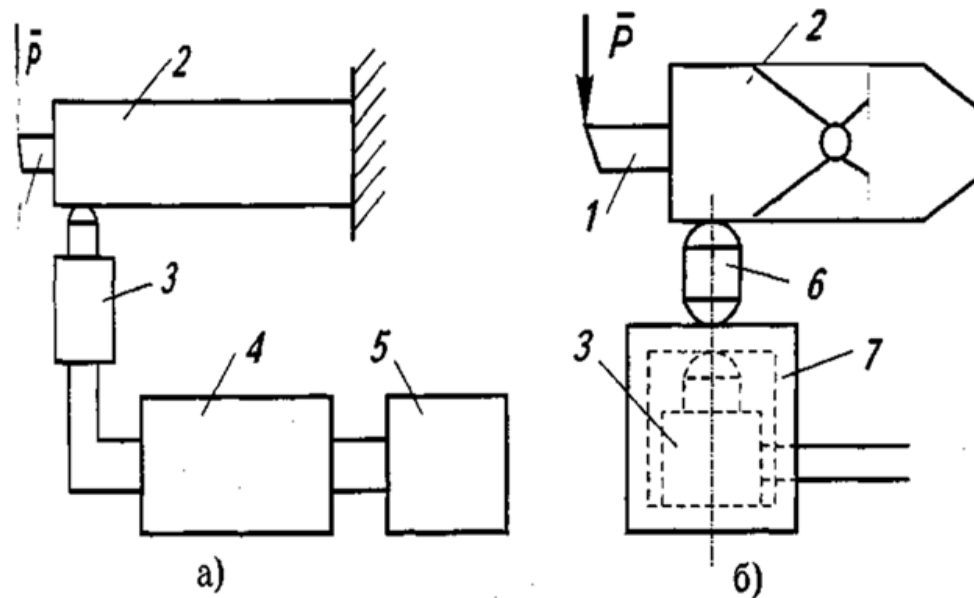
Принципові схеми динамометрів з пружною (а) і важільно-шарнірною (б) передаючими системами.: 1 - різець; 2 - різцетримач; 3 - давач; 4 - перетворювач; 5 - реєструючий пристрій; 6 – передаючий стержень; 7 – робочий пружний елемент
